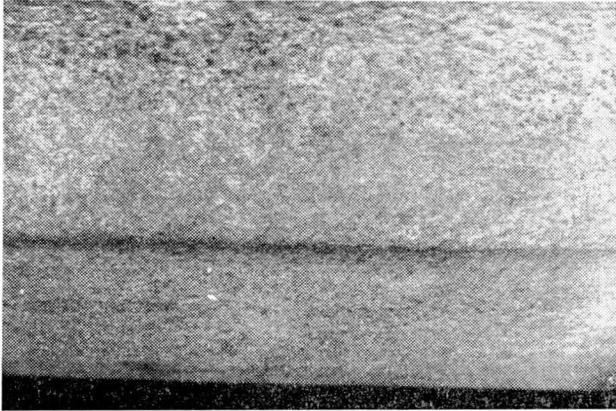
Superfície rugosa e defeito de laminação. 2 ×.
